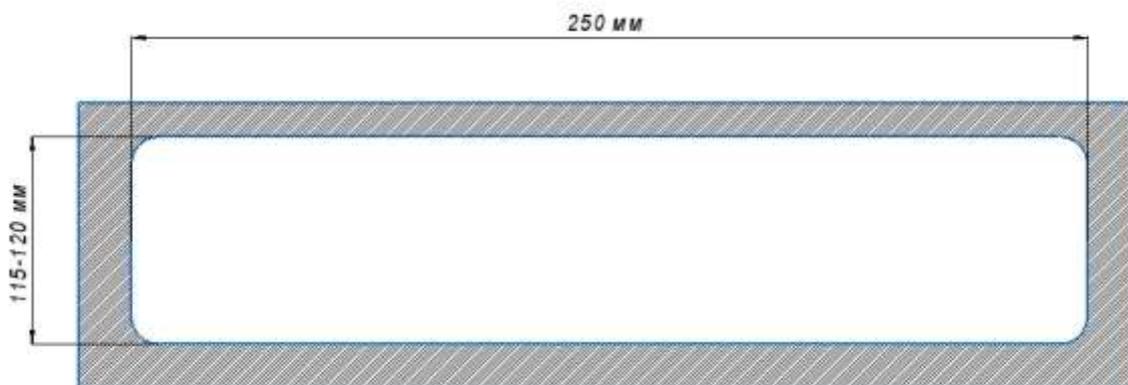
Пресс-форма для изготовления прямоугольной пластины
